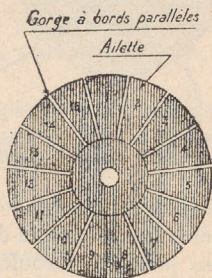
Carcasse pour enroulement « fond de panier ».
